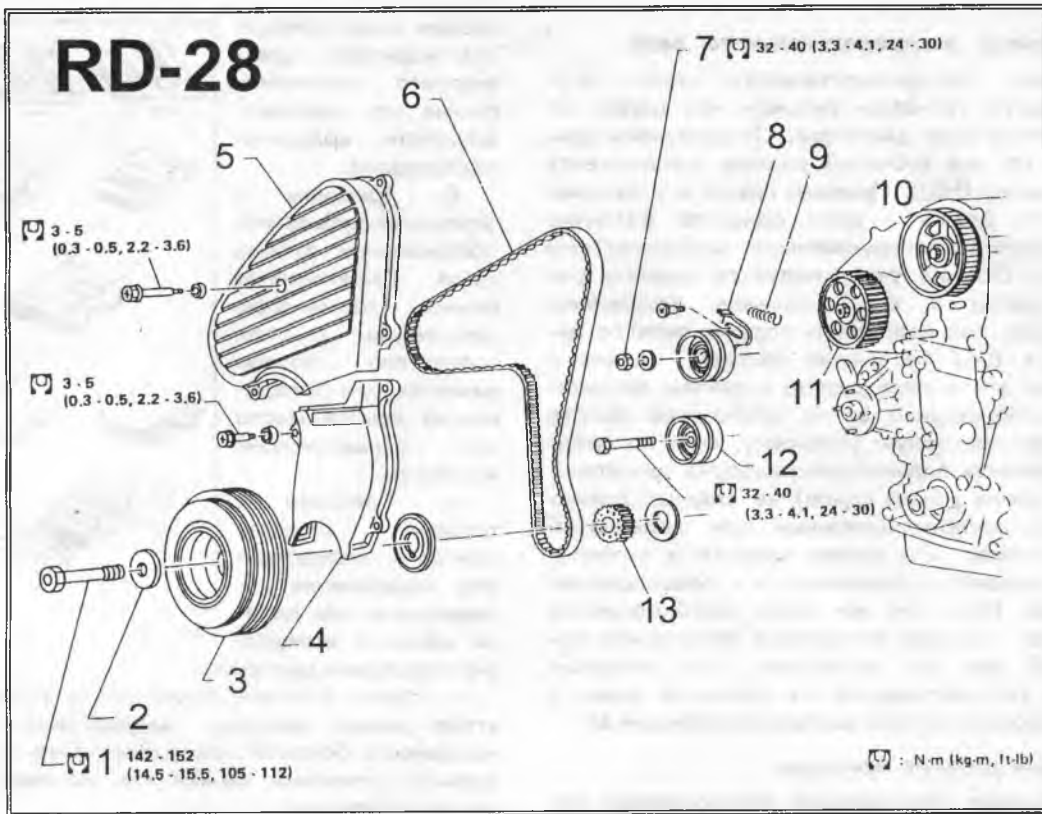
1. Болт. 2. Шайба. 3. Шкив для клинового ремня. 4. Нижняя крышка. 5. Верхняя крышка. 6. Зубчатый ремень. 7. Гайка фиксации натяжителя. 8. Натяжитель. 9. Пружина натяжителя. 10. Зубчатый шкив привода распределительного вала. 11. Зубчатый шкив привода ТНВД. 12. Опорный ролик. 13. Зубчатый шкив коленчатого вала.
